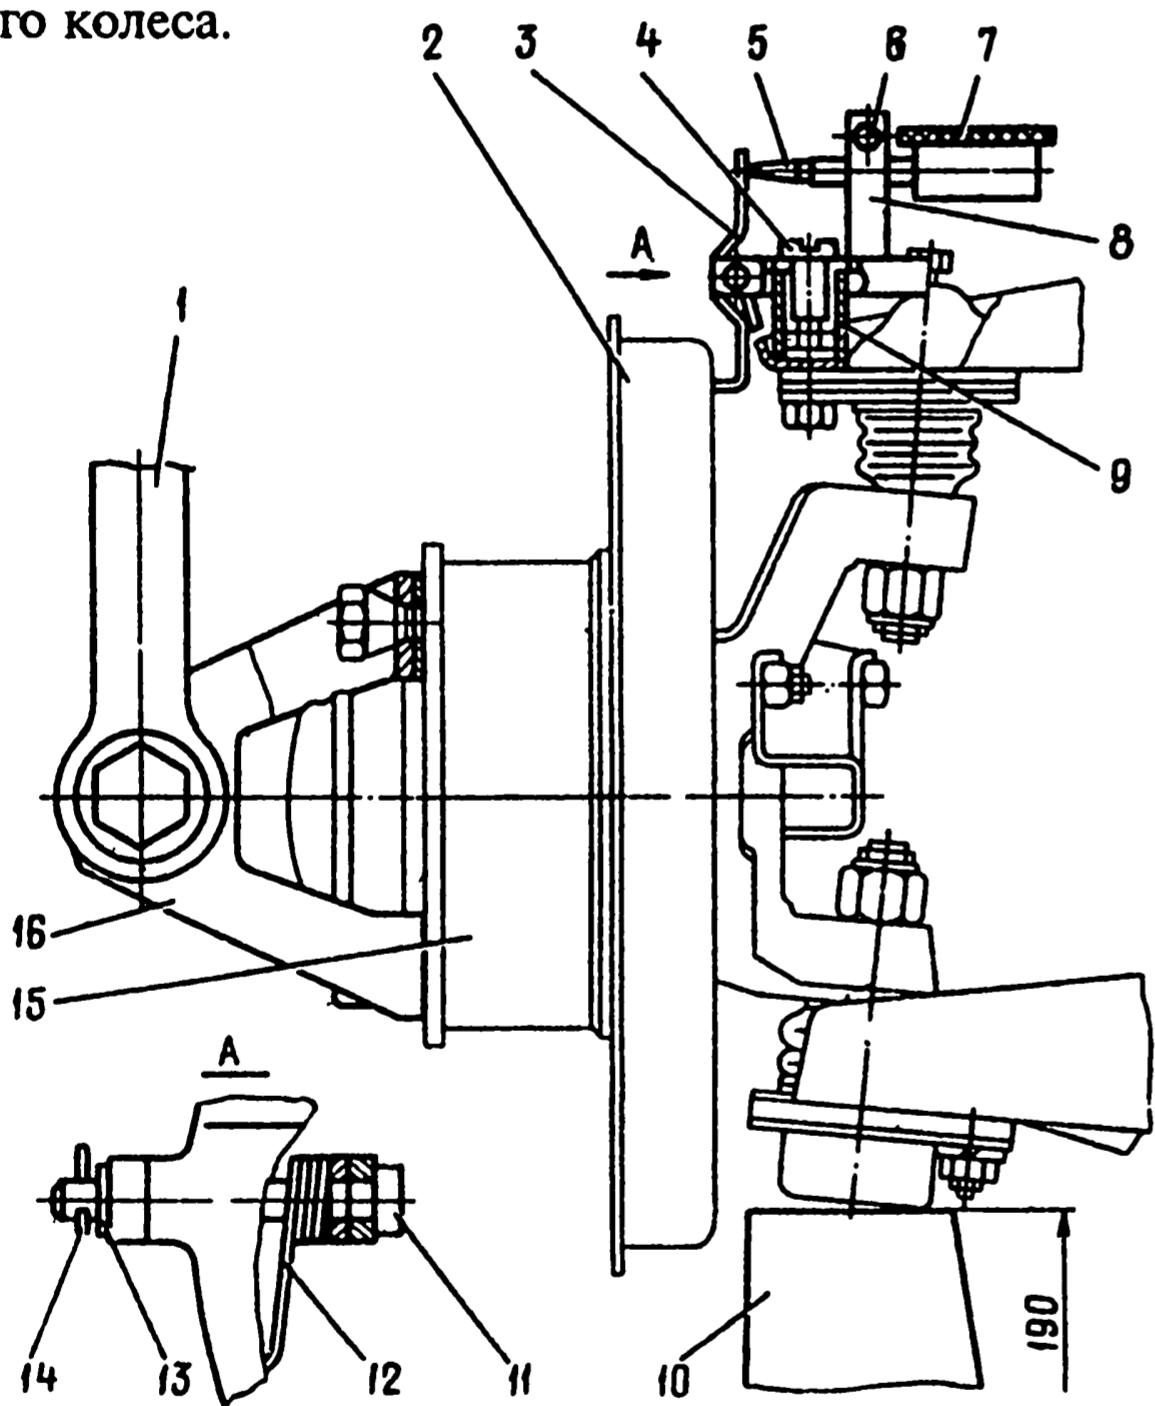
Замер зазора в верхнем шаровом шарнире приспособлением 02.8701.9500 (тормоз условно не показан): 1 - динамометрический ключ; 2 - защитный кожух тормоза; 3 - рычажок; 4 - винт; 5 - удлинитель индикатора; 6 - болт; 7 - индикатор; 8 - основание; 9 - втулка; 10 - колодка; 11 - ось; 12 - пружина; 13 - шайба; 14 - шплинт; 15 - ступица колеса; 16 - кронштейн
